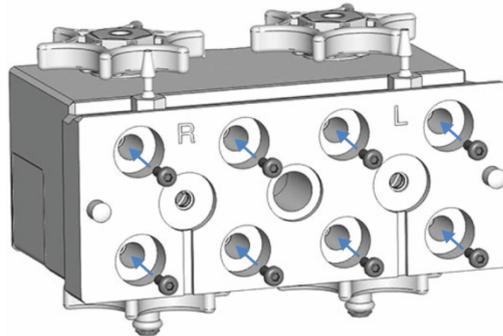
Tête de pompe avec plaque de rinçage des joints and et vis pour plaque
